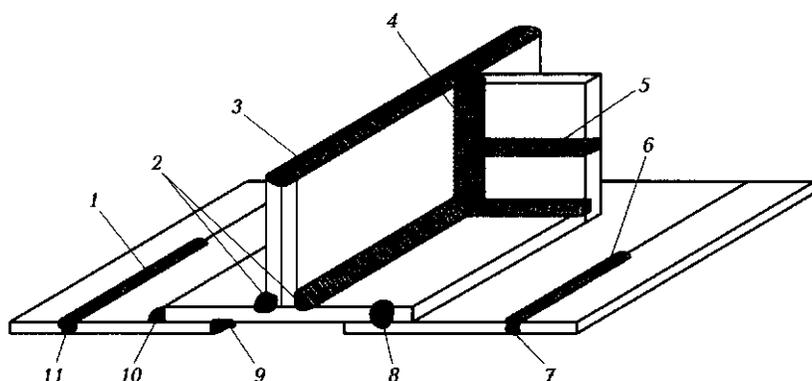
Положение в пространстве различных видов сварных швов:
